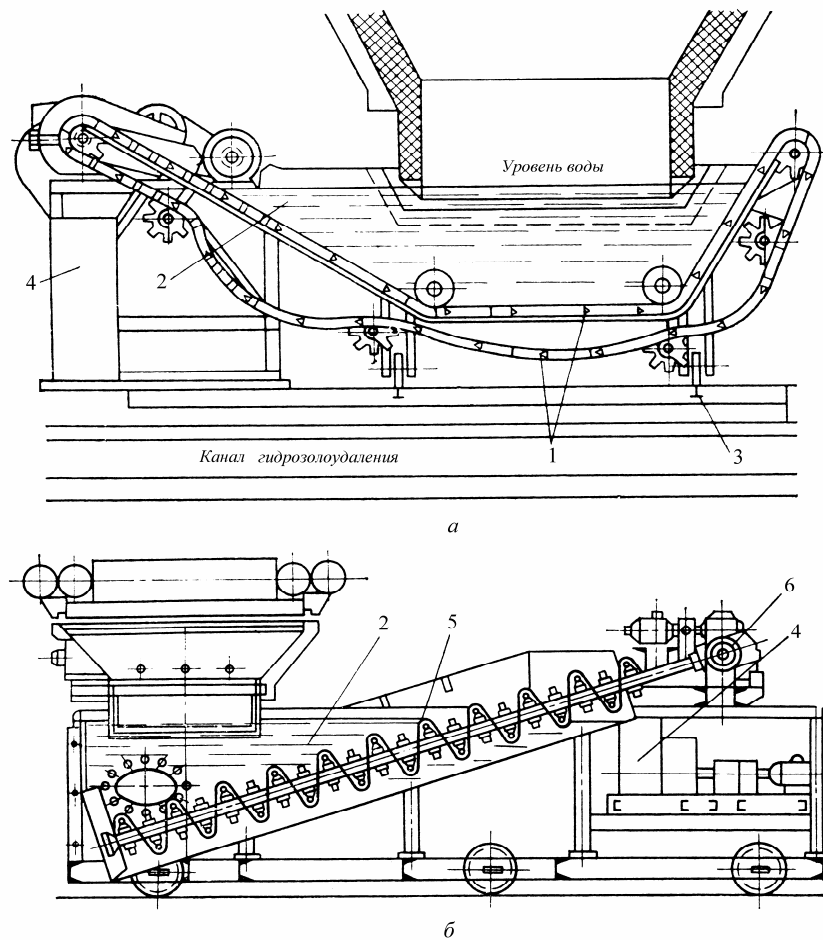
Устройства для механизированного непрерывного шлакоудаления: *а* – со скребковым транспортером; *б* – со шнеком; 1 – транспортер; 2 – ванна; 3 – рельсы; 4 – шлакодробилка; 5 – винтовой шнек; 6 – шарнир
